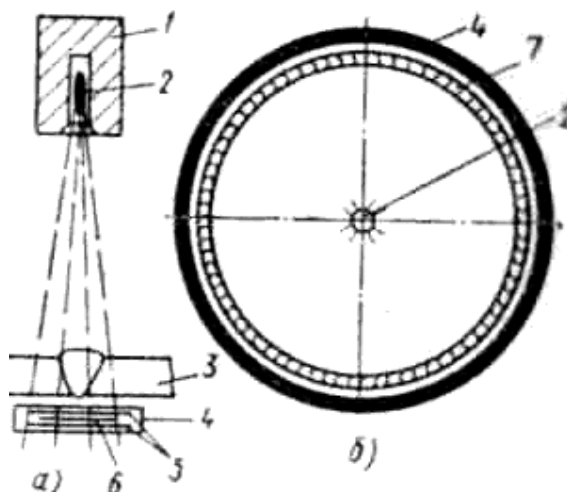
Схемы гамма-просвечивания: а — стыкового шва; б — кольцевого шва; 1 — свинцовый кожух; 2 — ампула; 3 — сварная деталь; 4 — кассета; 5 — экран; 6 — пленка; 7 — шов
